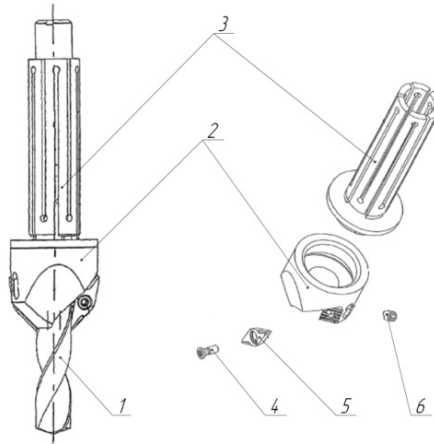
Свердло-зенківка фірми Seco Tools
